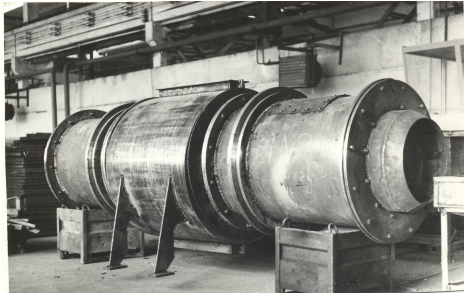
Барабан установки для непрерывной отделочно—зачистной обработки деталей в сборе с винтовым агрегатом
